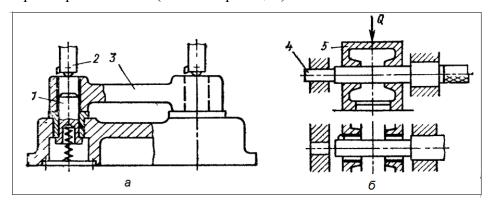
Схемы установки заготовок по обрабатываемым отверстиям: а – установка на подпружиненный палец; б – установка с помощью скалки
